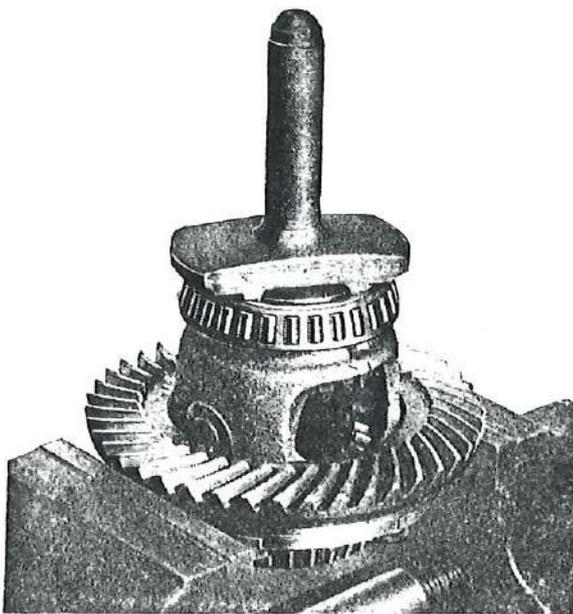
Montaje, mediante el útil A. 62027, del anillo interior del rodamiento a rodillos sobre la caja interna del diferencial.
